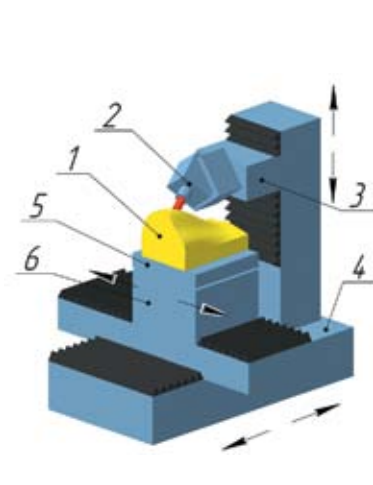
Фрезерный станок для объемного фрезерования с ЧПУ (тип 2):
